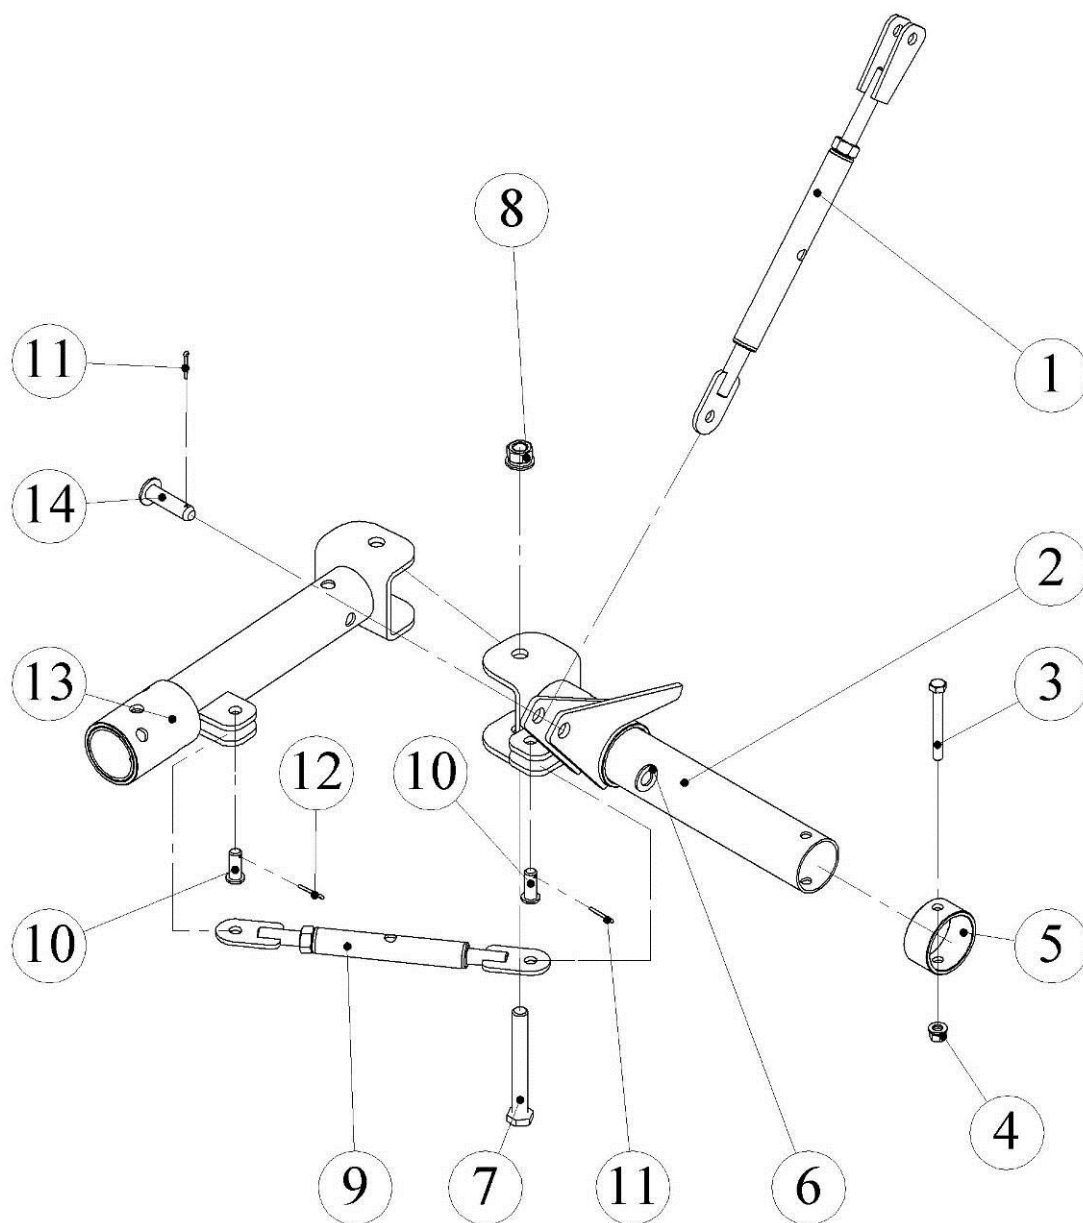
Рычаг поворотный и рычаг подвижный
